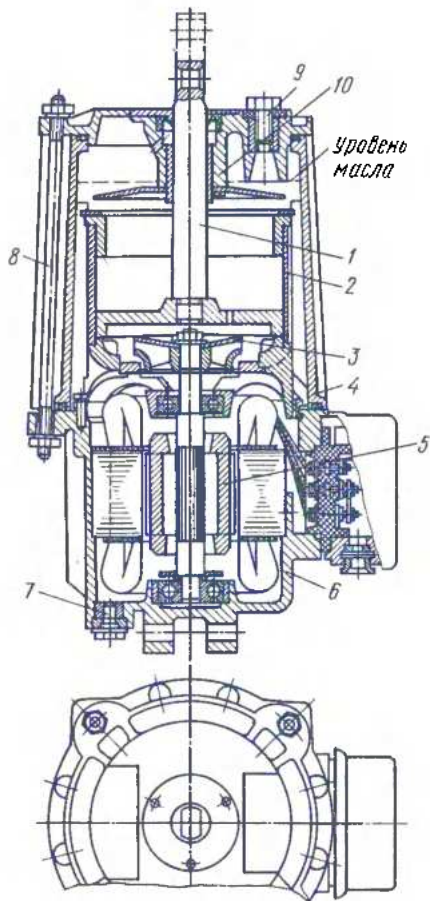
Электрогидравлический толкатель: 1 — поршень со штоком, 2 — гильза, 3 — крыльчатка центробежного насоса, 4 — корпус, 5 — электродвигатель, 6, 10 — нижняя и верхняя крышки, 7, 9 — пробки, 8 — шпилька
